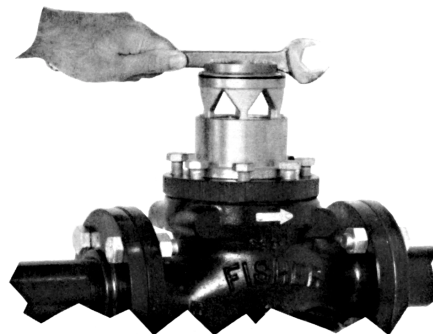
Опорный уплотнитель и/или удаление кожуха или использование корпуса в качестве зажима
